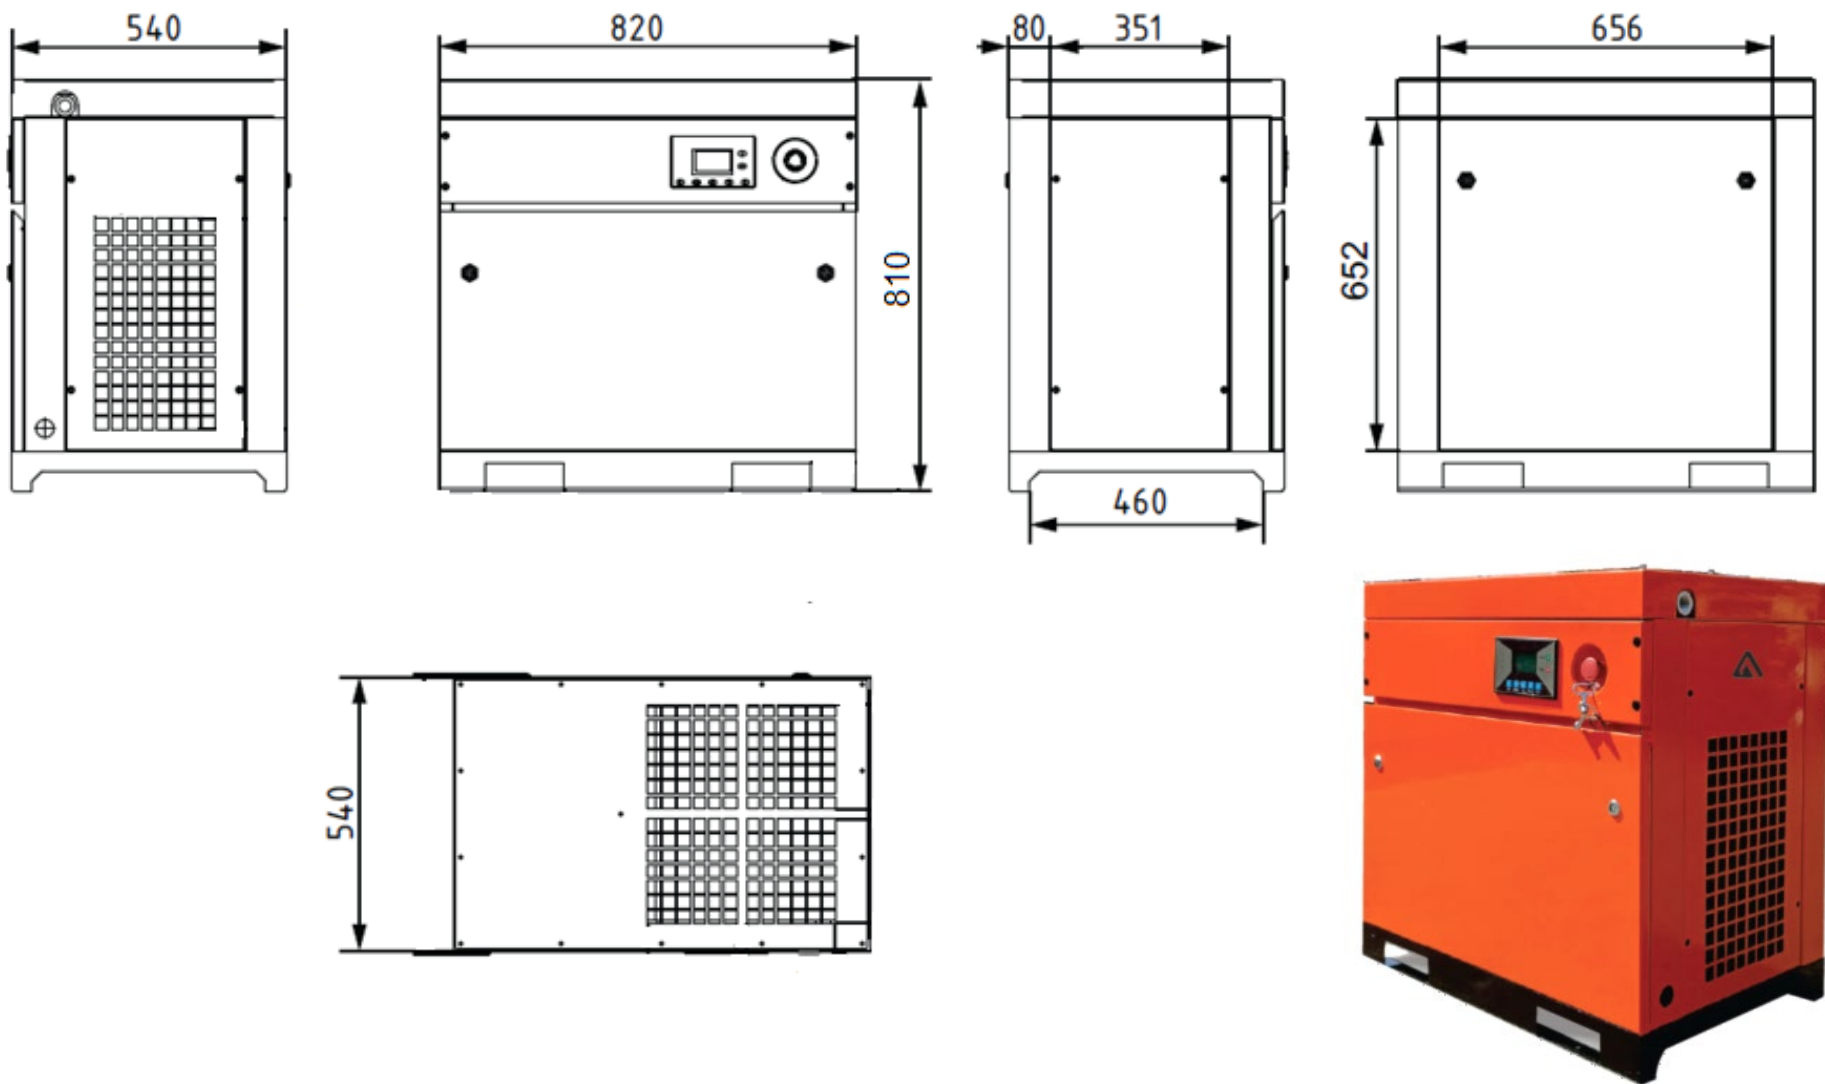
Общий вид, габаритные размеры станции компрессорной ЗИФ-СВЭ типа АРМ с двигателем 7,5 кВт
